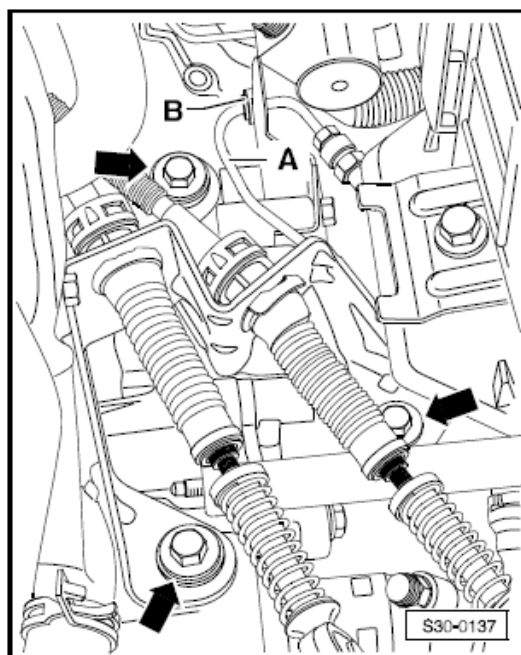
Контропори гнучких валів коробки зміни передач
